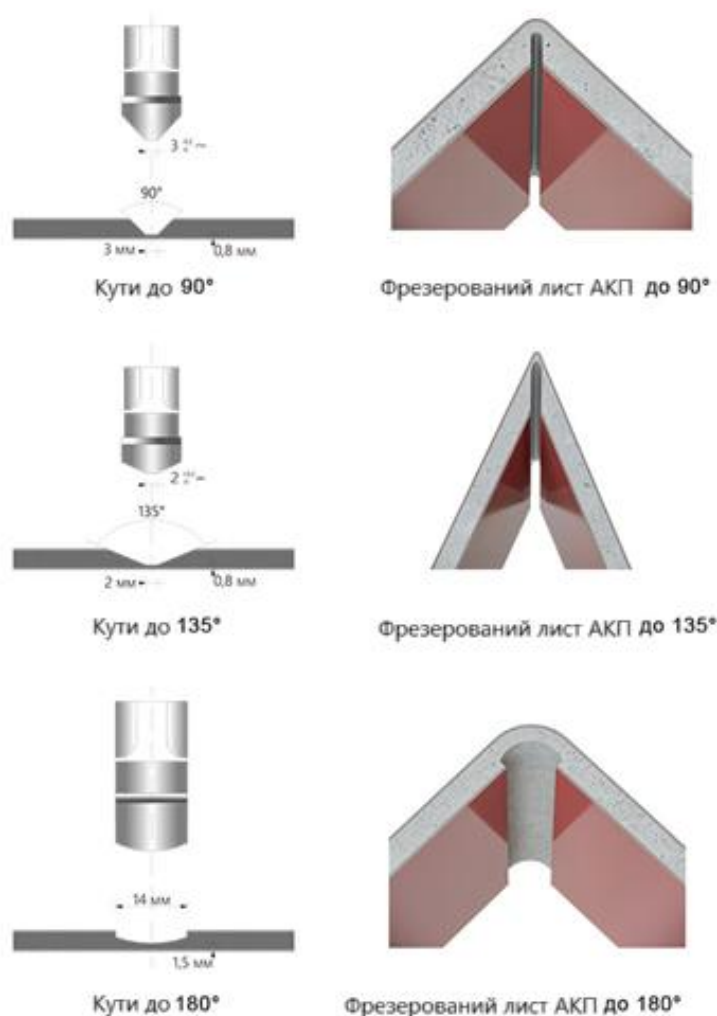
Типи пальцевих фрез для обробки АКП
